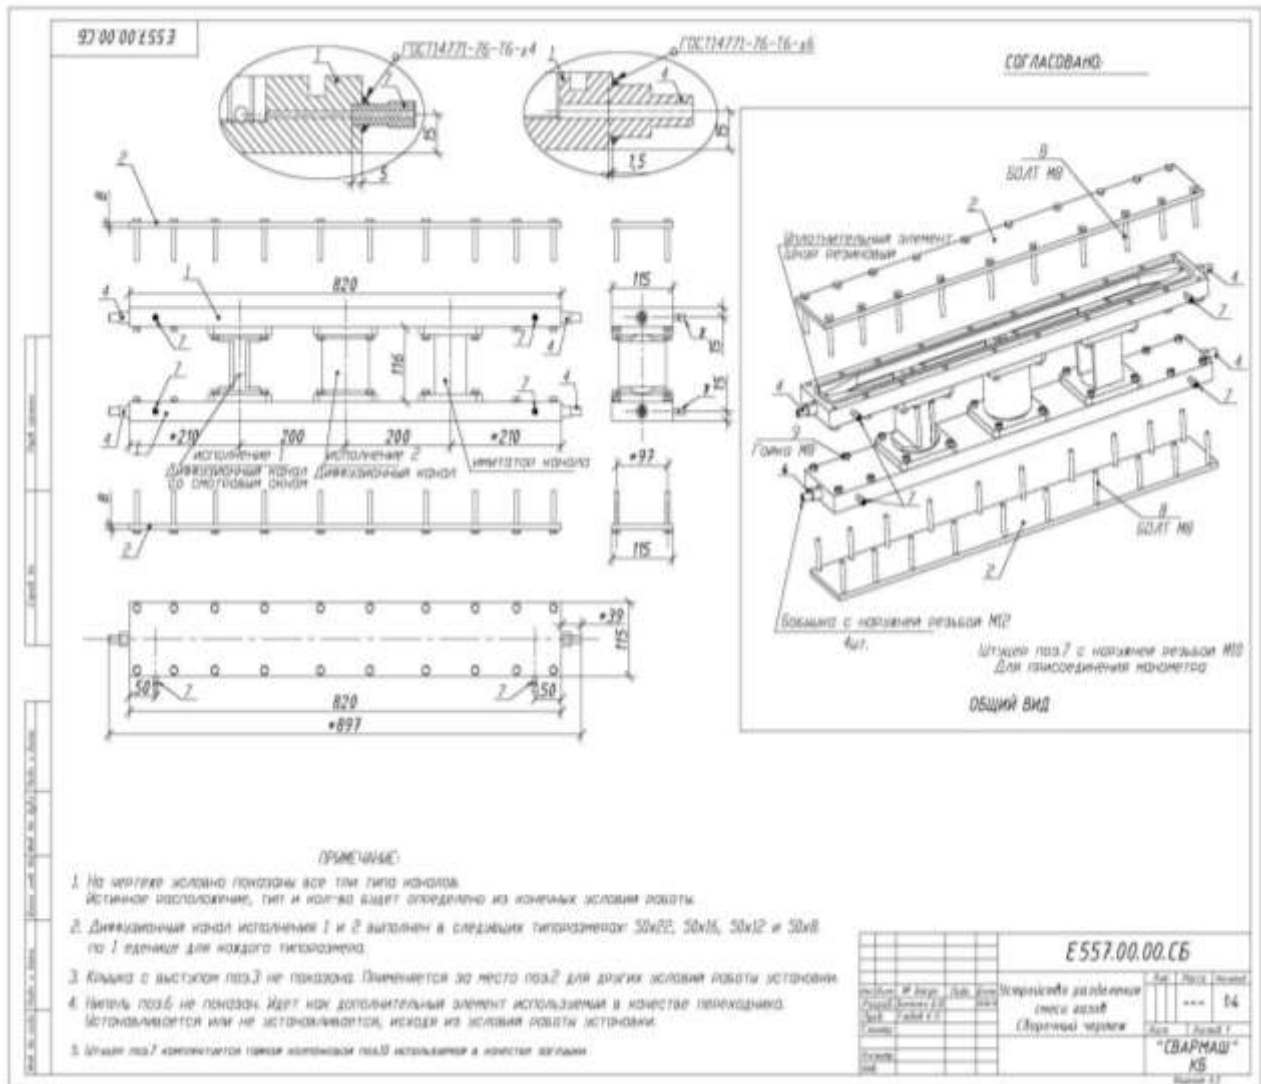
Сборочный чертеж модуля опытного устройства по разделению природных газов.
